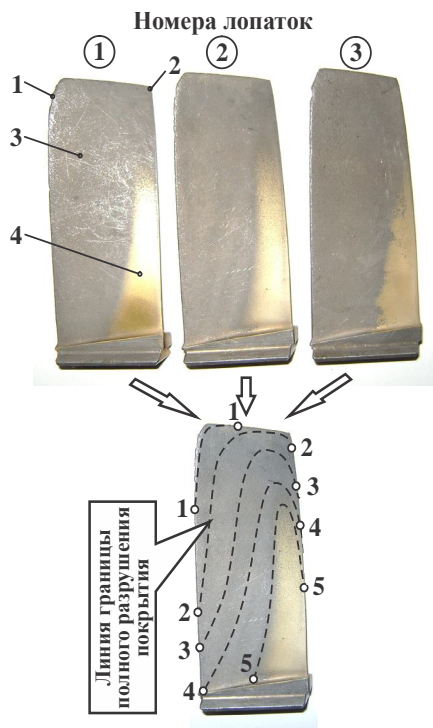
Схема неравномерного разрушения нитрид титанового покрытия поверхности пера лопатки:
